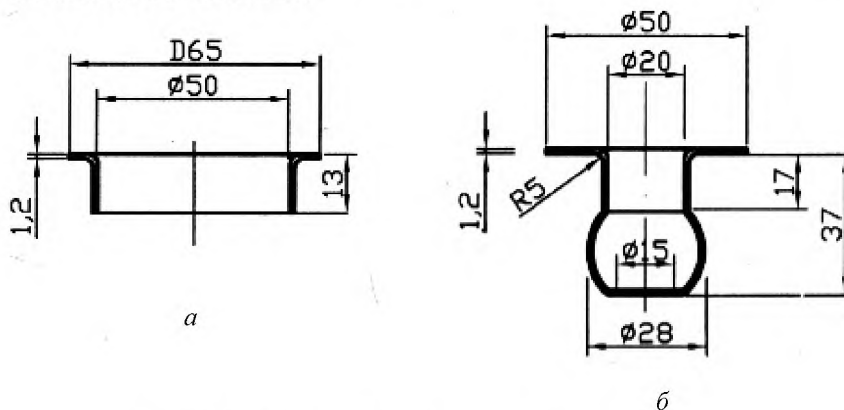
Элементы разделенной детали ступицы: а – деталь 1 (верхняя часть); б – деталь 2 (нижняя часть)
